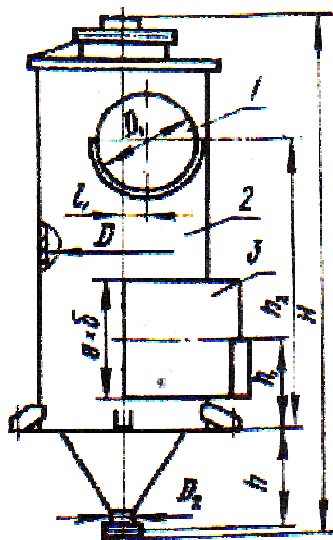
Каплеуловитель типа КЦТ: 1 – выходной патрубок; 2 – корпус; 3 – входной патрубок
